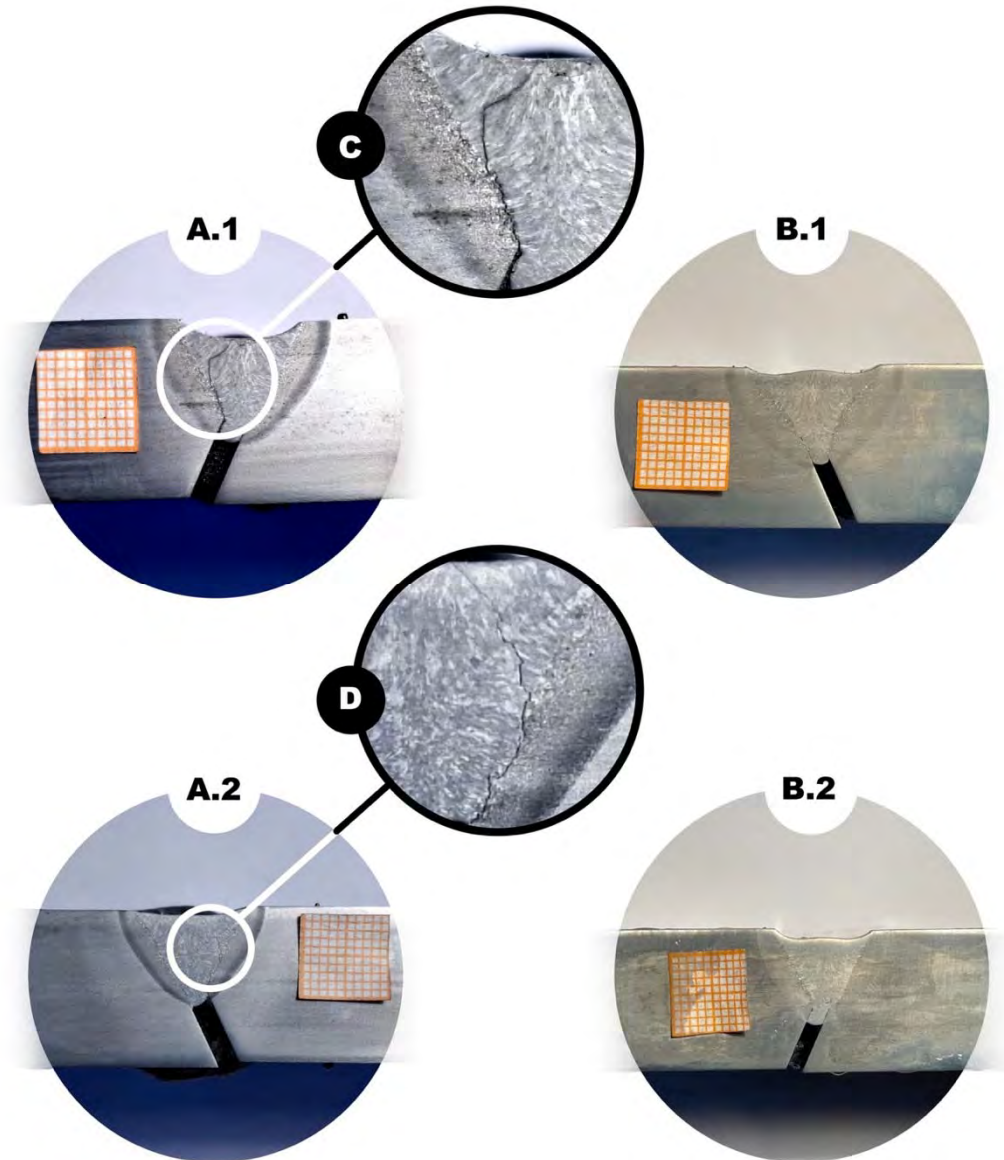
Макрошлифы технологической пробы Тэккен: А – сварка с традиционной защитной газовой смесью (82 % Ar + 18 % CO₂); В – сварка с введением в состав защитной газовой смеси SF₆; С, D – трещины в сварном соединении
